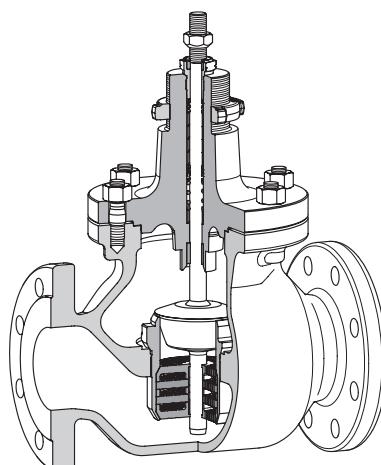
· Клапан тип 3251 с гарнитурой AC-2 Trim и четырьмя дроссельными шайбами
